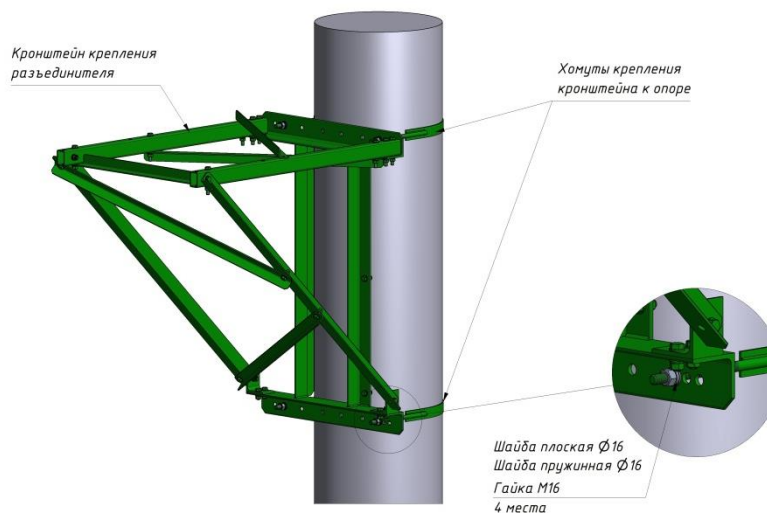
Крепление кронштейна разъединителя на бетонные опоры СК 22
